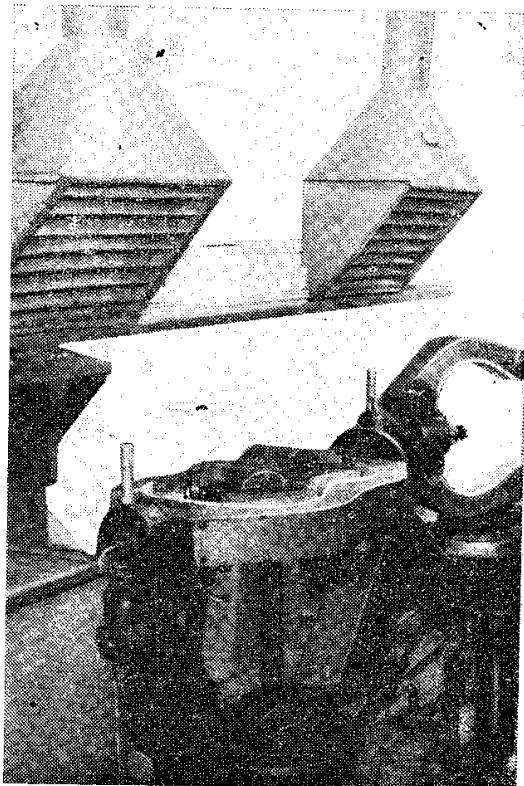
Пневматические ваймы с электрическим нагревом для сборки рамки гитарного корпуса
